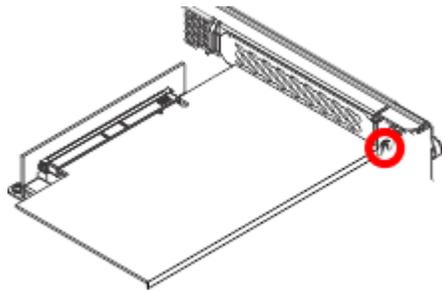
Schraube an der Adapterkassettenhalter entfernen
